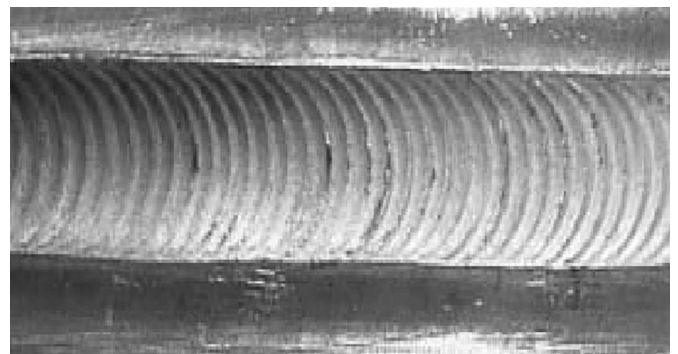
Внешний вид сварного соединения, выполненного автоматической сваркой
